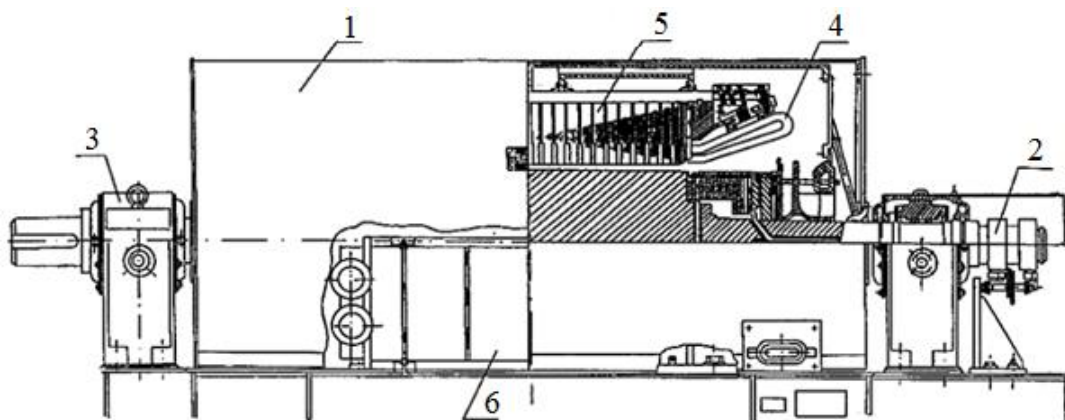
Электродвигатель СТД-4000-2: 1 – Электродвигатель; 2 – редуктор; 3 – центробежный нагнетатель; 4 – обвязка гпа; 5 – местный щит управления; 6 – АВО масла
